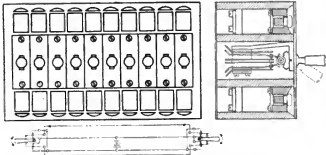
Maschinentelegraph (Böker, Krüger & Co.).
